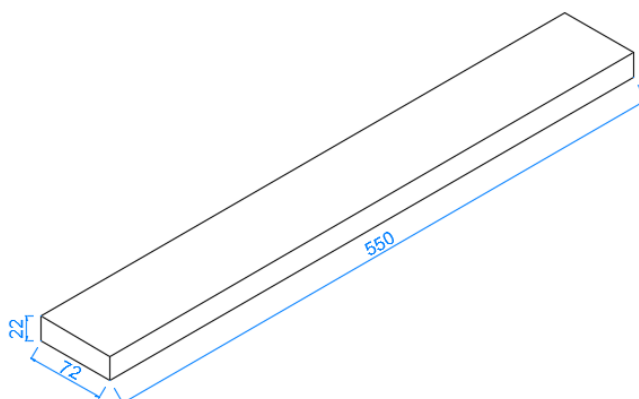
Dimensiones en mm de probetas para ensayo a flexión
